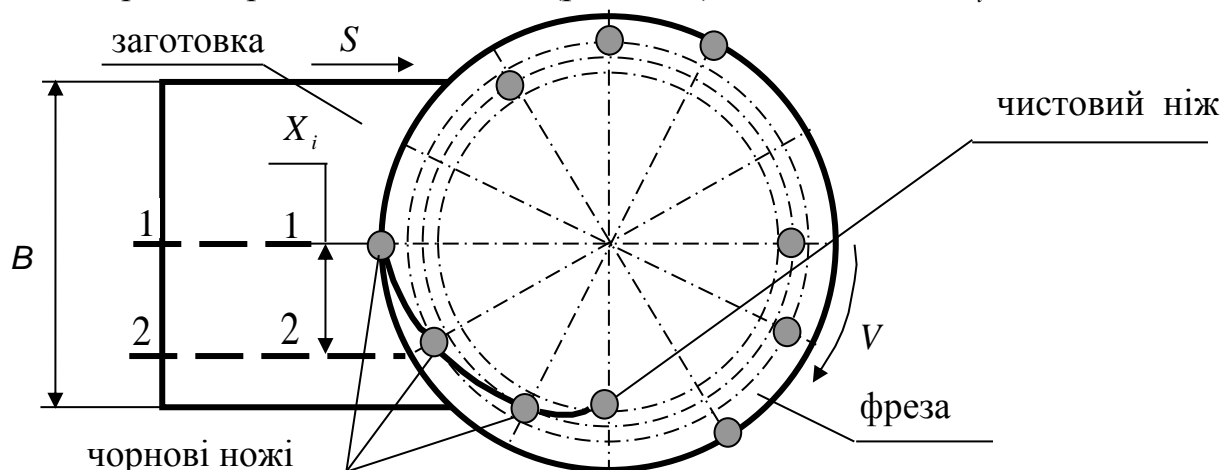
Схема розташування фрези відносно заготовки
